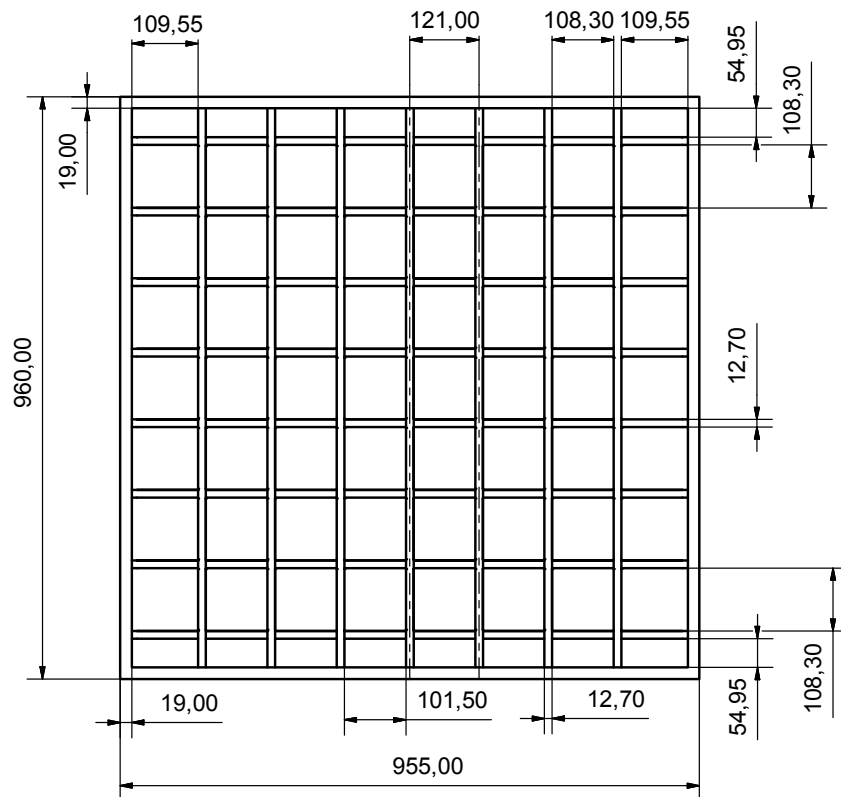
Plano detallado malla activa con medidas características. Medidas en milímetros.
